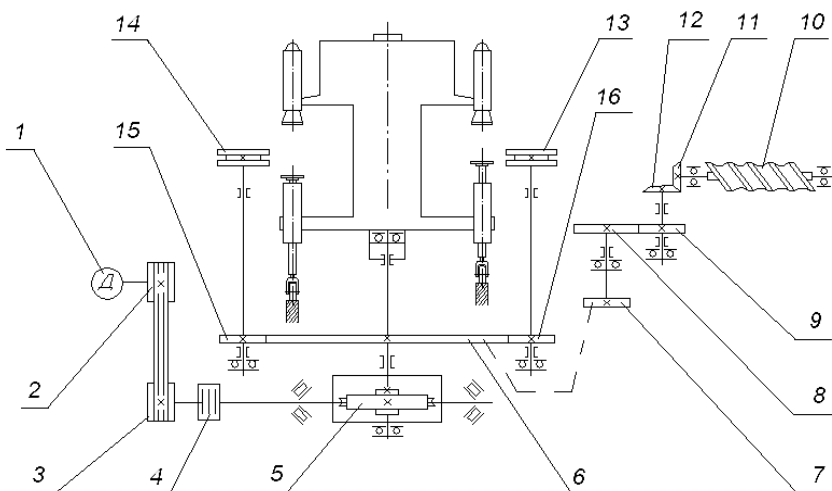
Принципова кінематична схема роторної фасувальної машини: 1 – електродвигун; 2, 3 – шківи; 4 – муфта; 5 – редуктор; 6–9, 15, 16 – шестерні; 10 – шнековий ділильний пристрій; 11, 12 – зубчаті колеса; 13, 14 – завантажувальні і розвантажувальні зірочки відповідно
